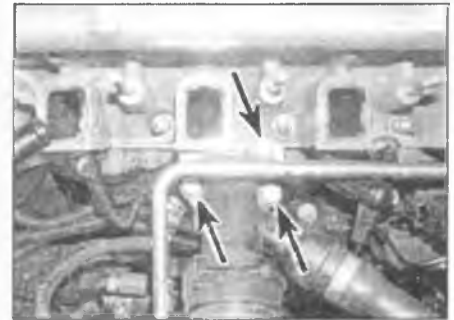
Выверните три болта (см. стрелки) и отсоедините соединитель шланга охлаждающей жидкости от головки цилиндров
